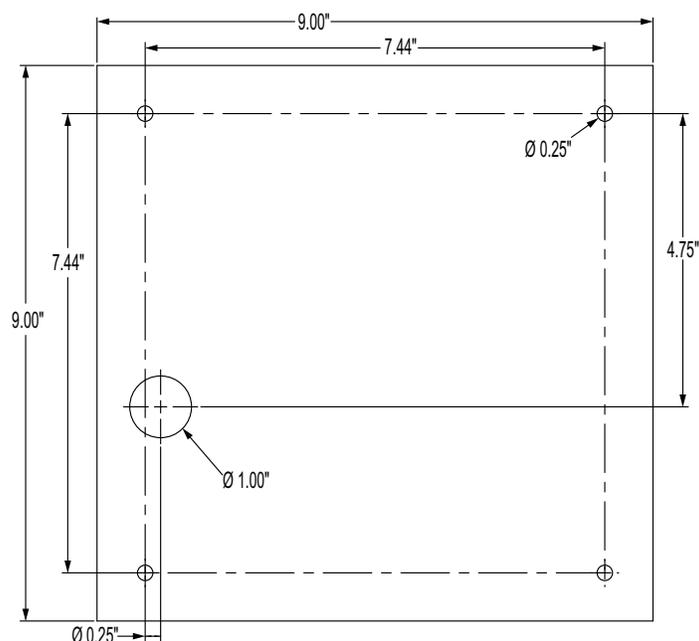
Dimensioni della versione da 7" con montaggio a pannello (con tastiera)
